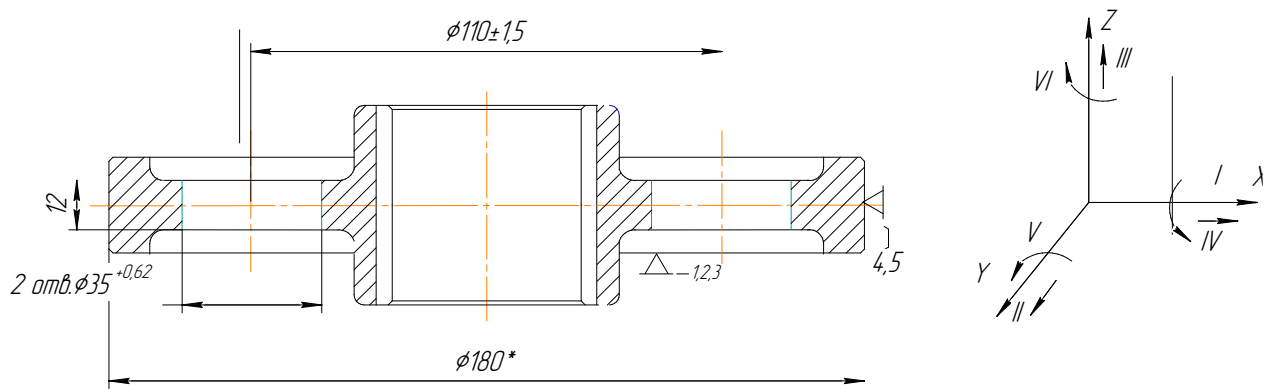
Схема базування заготовки у самоцентруючі призми
